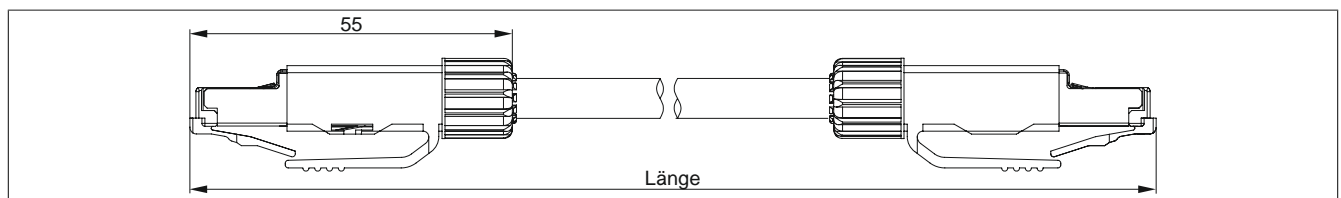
5CASD3.xxxx-00 - Abmessungen
